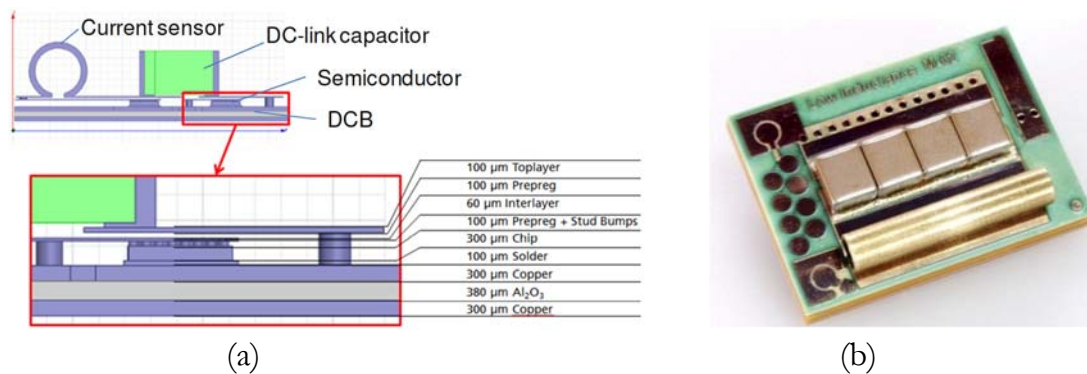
(a) vue en coupe de l'assemblage et (b) module fini [26][27]
